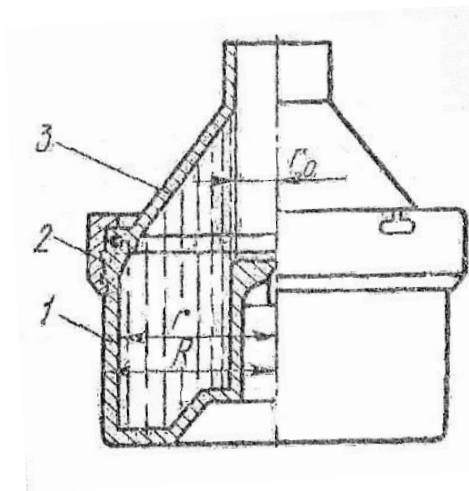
Барабан сепаратора: 1- корпус, 2-зеднувальне кільце, 3- кришка.
